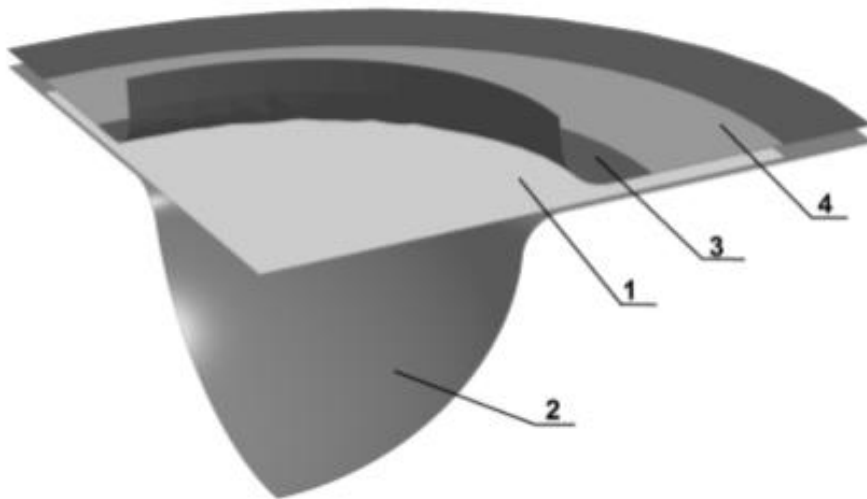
Геометрична модель інтенсифікованої ЕГІ витяжки тонколистового й особливо тонколистового металу: 1 – листова заготовка; 2 – матриця; 3 – інерційний розгладжувач; 4 – обмежувач
